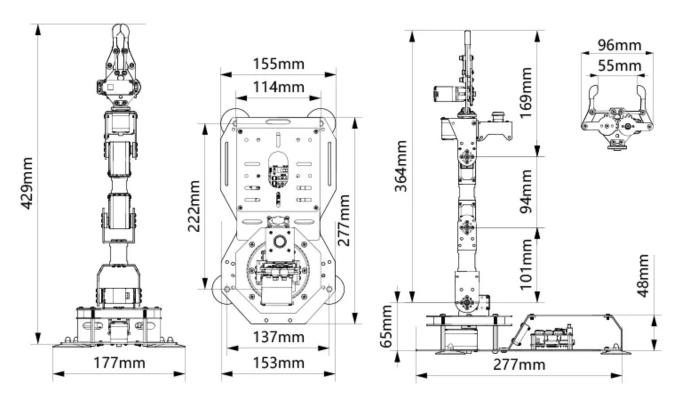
Габаритные чертежи робота-манипулятора АF.
